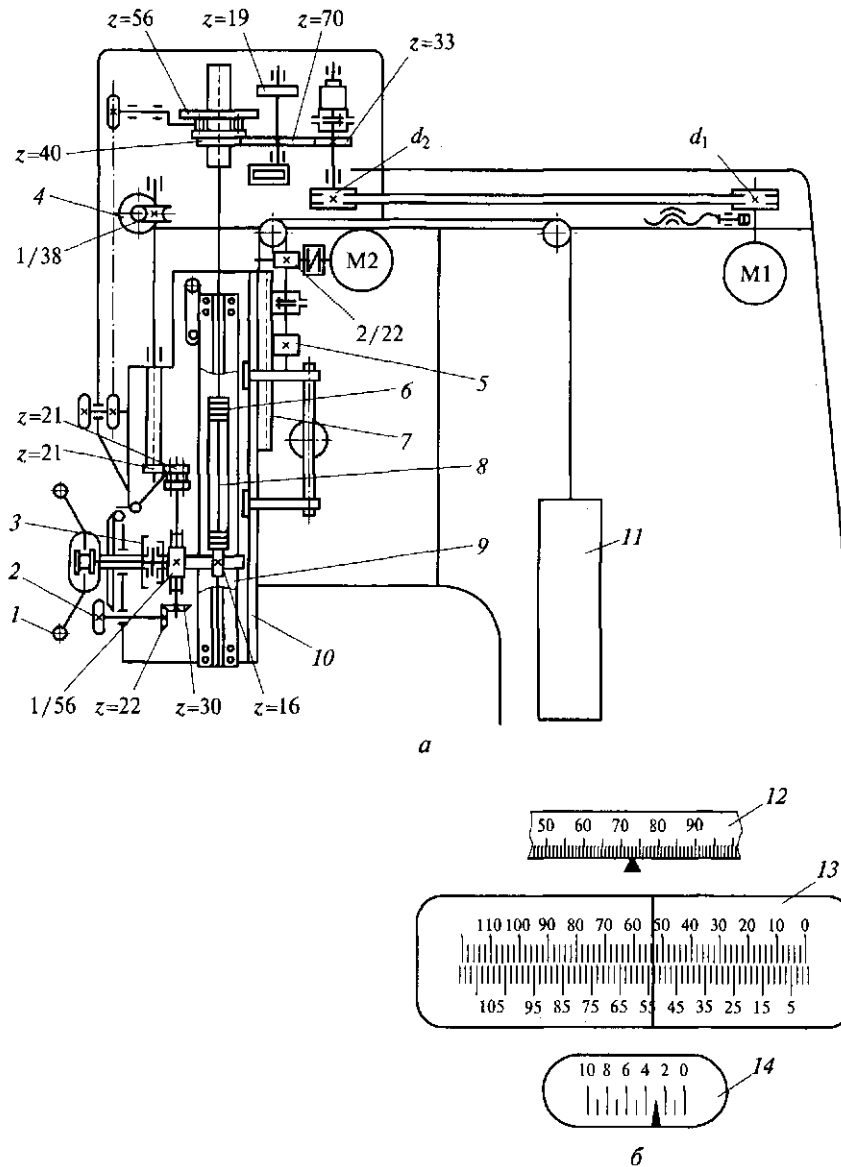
Кинематическая схема шпиндельной бабки координатно-расточного станка (а) и шкалы его оптического устройства (б):
